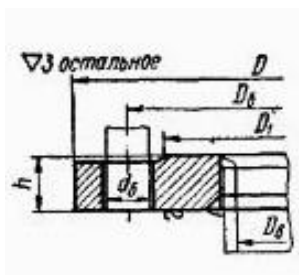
Фланец для стальных сварных аппаратов
